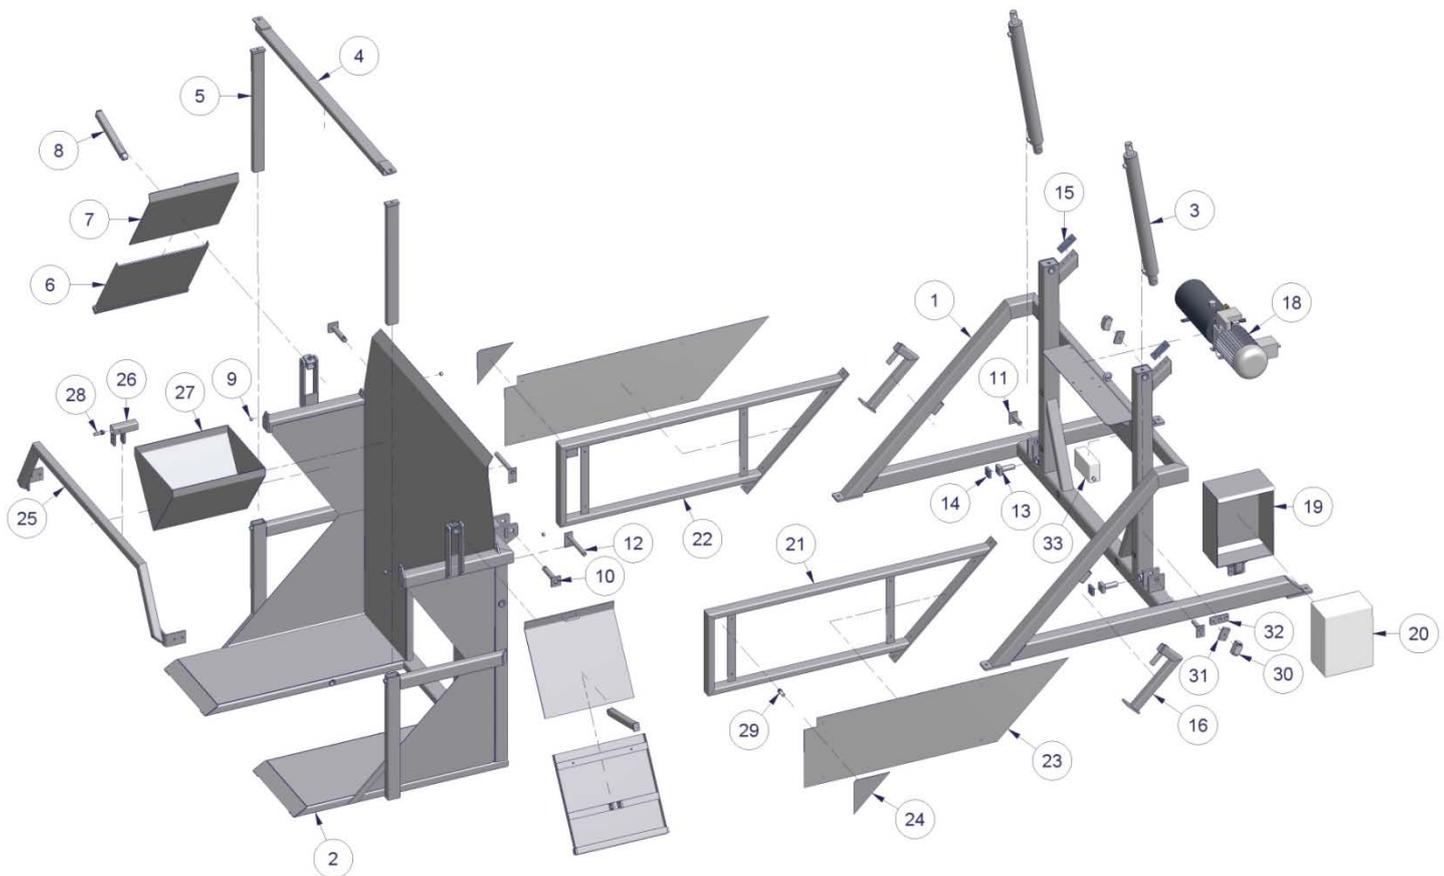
Vue éclatée des pièces pour le modèle K60-AKB
